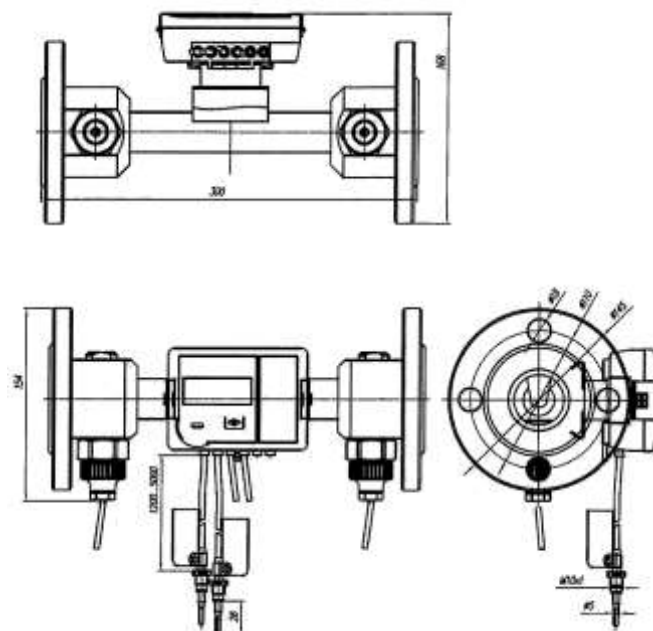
Присоединительный размер к трубопроводу DN40, длина L =300 мм
